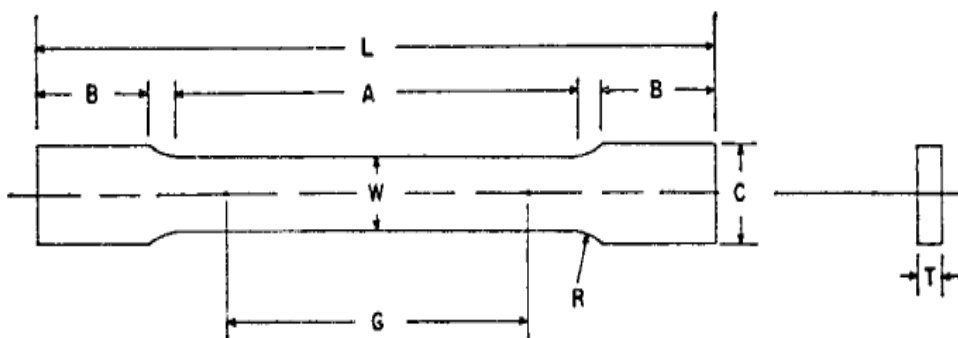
CROQUI PARA USINAGEM CORPO PROVA DE TRAÇÃO (ADAPTADO ASME IX)
